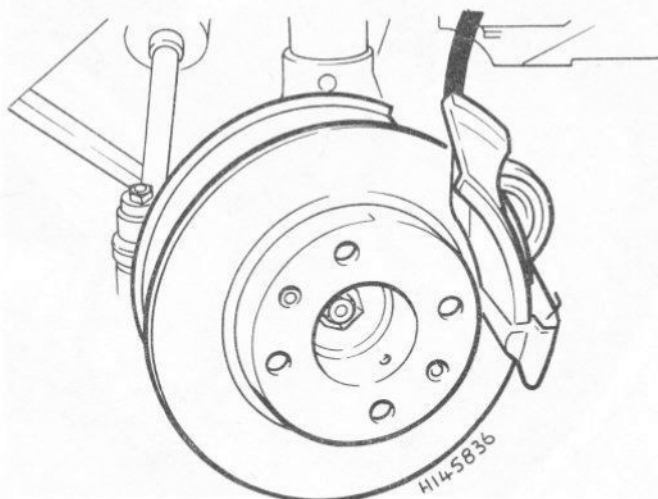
Dépose d'un disque de frein (Sec 6)
